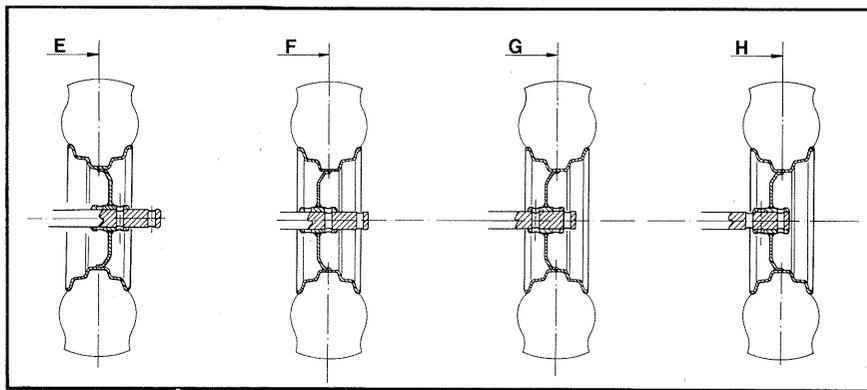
Schema carreggiate 290 - 330 - 390.
